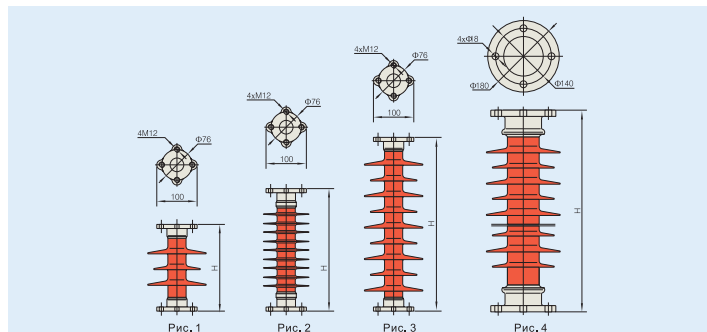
Внешний вид и размеры сборных штыревых изоляторов
